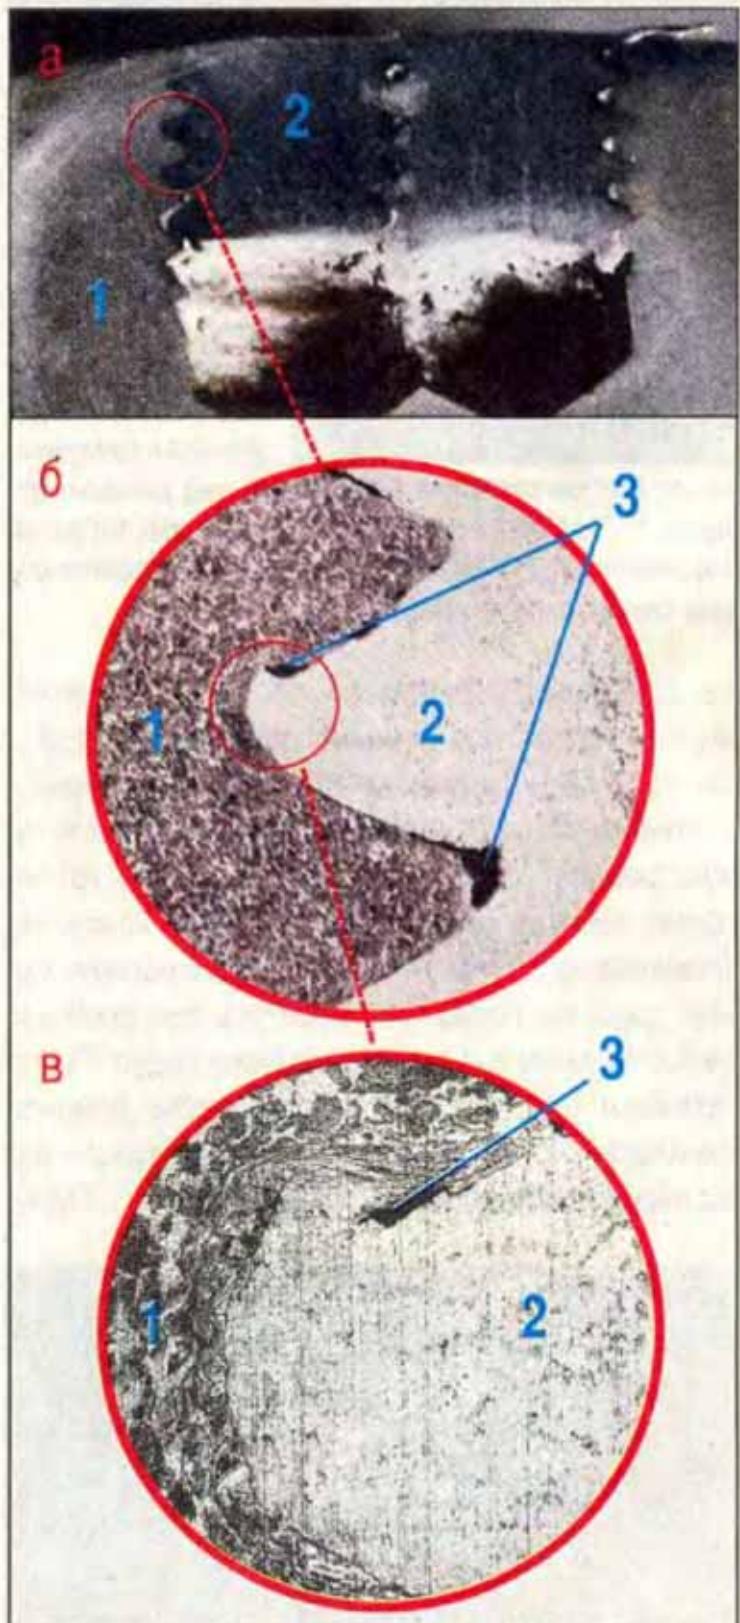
Разрез шва, полученного проковкой завернутых конических болтов-заглушек: а – отшлифованный образец, вырезанный из шва; б – граница уплотнения металла ремонтируемой литой детали и металла резьбовой заглушки; в – зона пластической деформации, прилегающая к границе уплотнения; 1 – деталь; 2 – конический болт-заглушка; 3 – термостойкий полимер.
